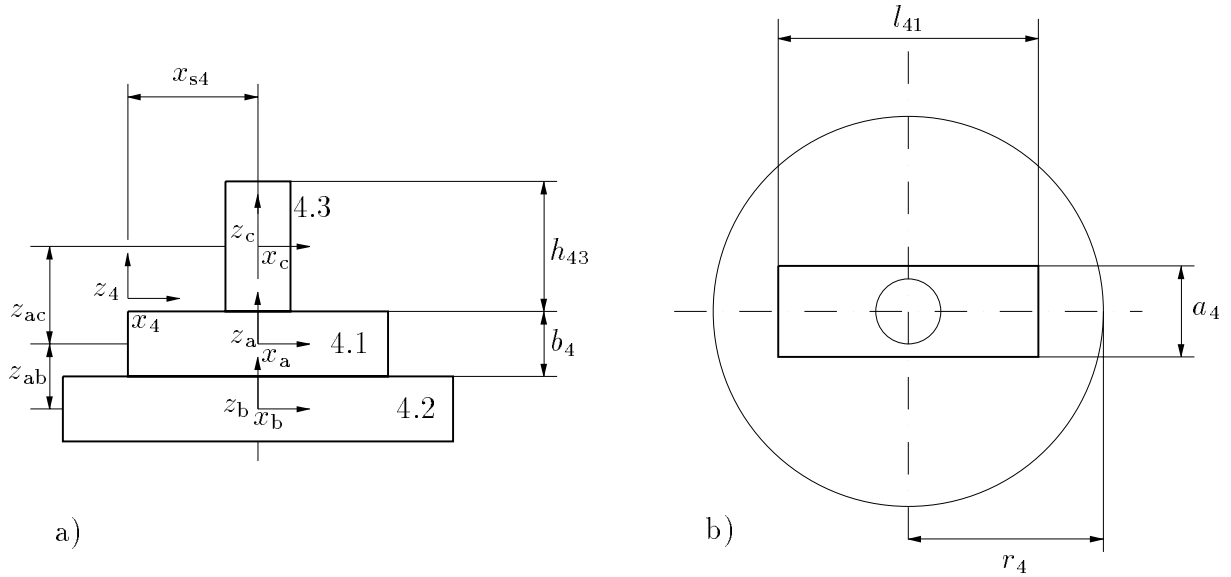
Glied 4 a) Seitenansicht; b) Draufsicht
